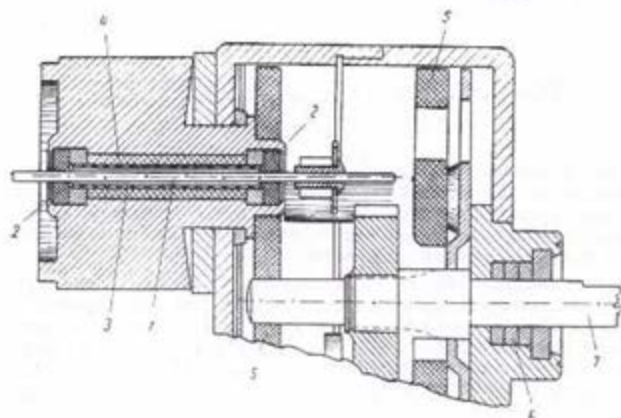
Secțiune prin cutia motorului sincron cu autopornire.
